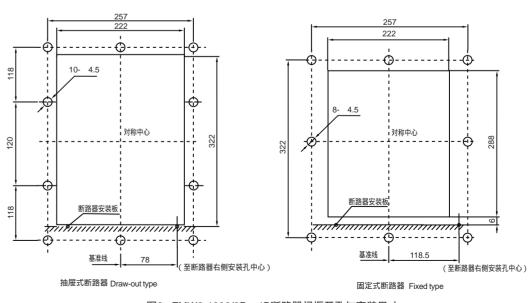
ZMW2-1600/3P、4P断路器门框开孔与安装尺寸 Figure 6 ZMW2-1600/3P、4P Door frame size& Mounting hole
